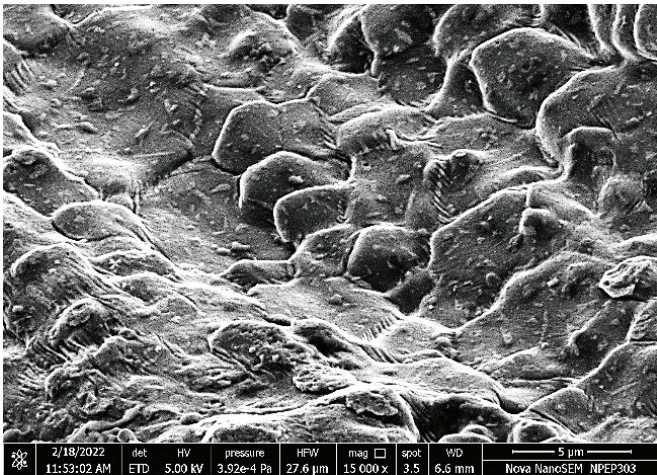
РЭМ-изображения поверхности излома UVaFSWed-соединений AA7075, подвергнутых дробеструйной обработке
